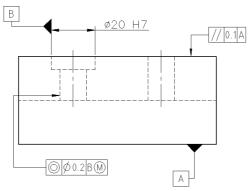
Exemplos de Tolerânciamento Geométrico
